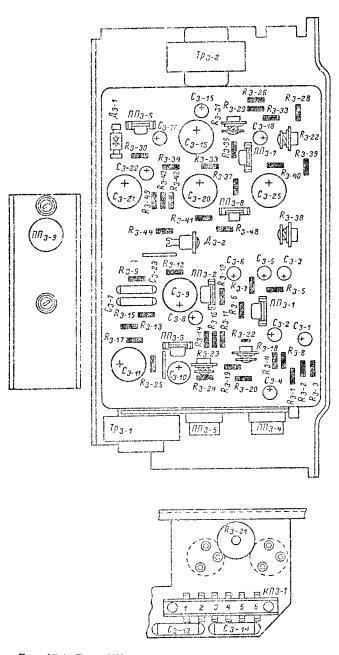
Блок УНЧ и кадровой развертки телевизора «Вечер» (вид со стороны деталей).
